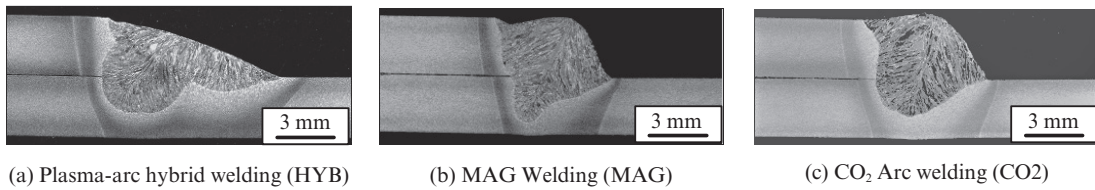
重ね隅肉溶接疲労試験片の溶接線垂直方向の断面マクロ組織
